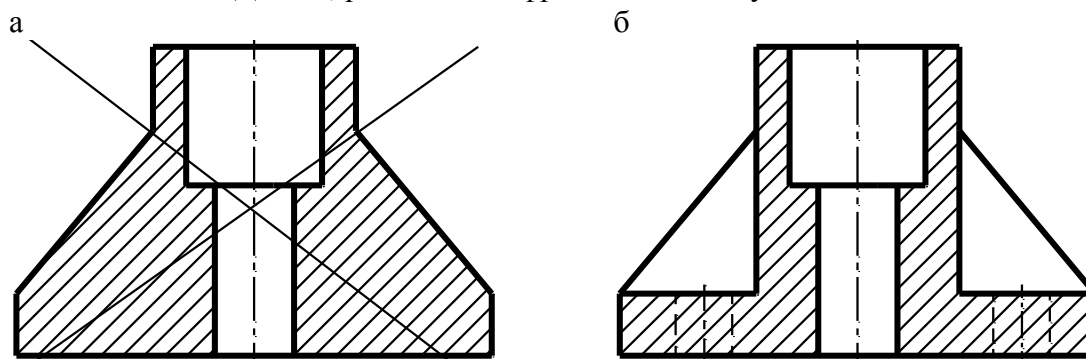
а – неправильно выполненный разрез вдоль тонких стенок, б – правильно выполненный разрез
